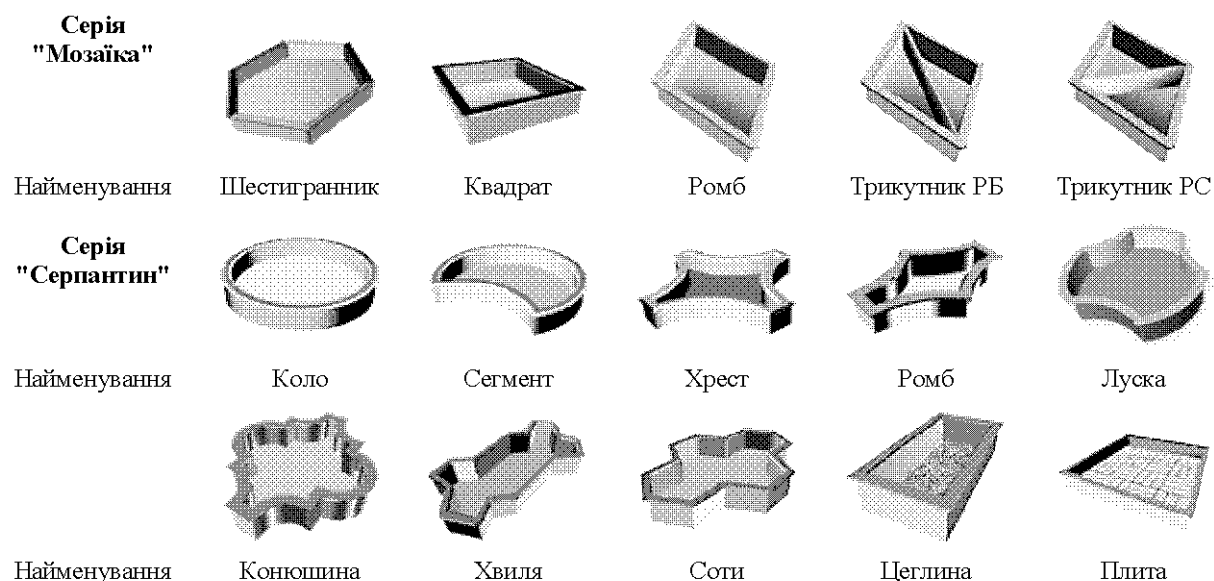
Форми для виготовлення ФЕМ методом вібролиття.
